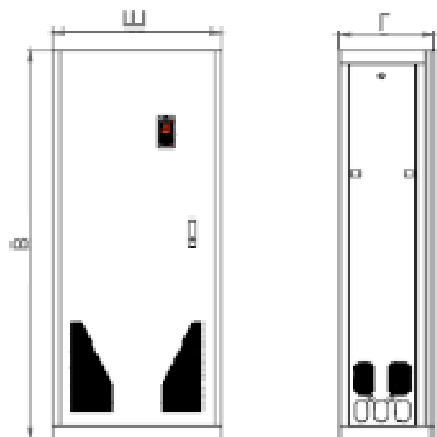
Габаритный чертеж преобразователя частоты модели С
